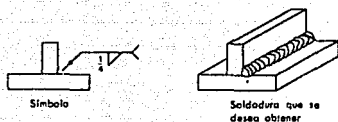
Soldadura de filete del lado de la flecha
